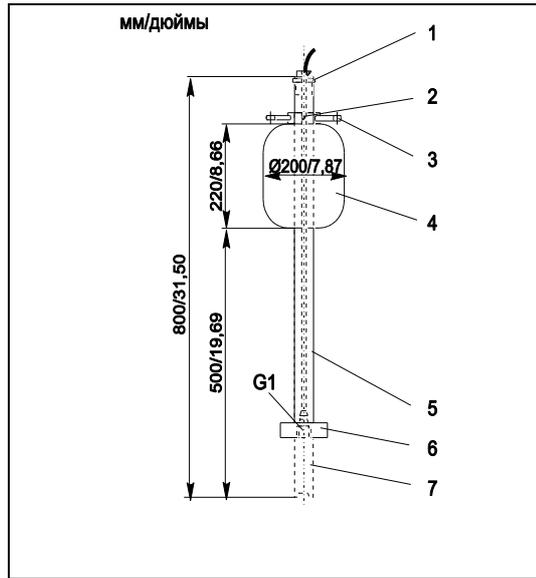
Вертикальное крепление для монтажа на краю бассейна
